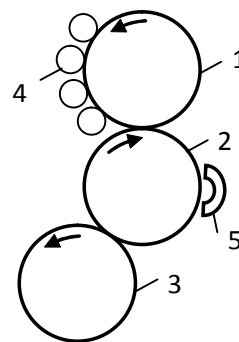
Схема расположения сушильного устройства: 1 – формный цилиндр; 2 – офсетный цилиндр; 3 – печатный цилиндр; 4 – накатные валики красочного и увлажняющего аппаратов; 5 – сушильное устройство
